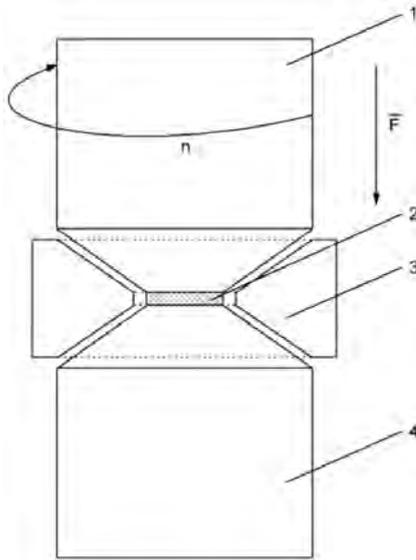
Схема расположения деформирующего инструмента и образца в наковальнях Бриджмена, где  $F$  - вектор прилагаемой силы, а  $n$  - угол поворота (1 - верхний поворотный пуансон, 2 - образец, 3 - упорное кольцо, ограничивающее диаметр деформируемого образца в горизонтальной плоскости, 4 - нижний неподвижный пуансон)
